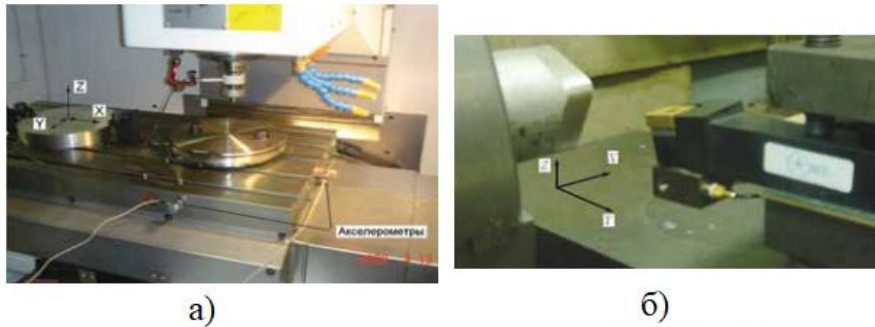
Приклади використання акселерометрів: а) на столі фрезерного верстата, б) на токарному різці
